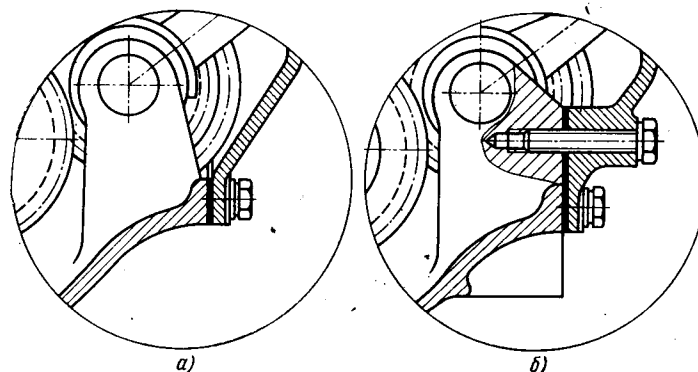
Крепление боковой крышки коробки передач к картеру: а — старая конструкция; б — новая конструкция
